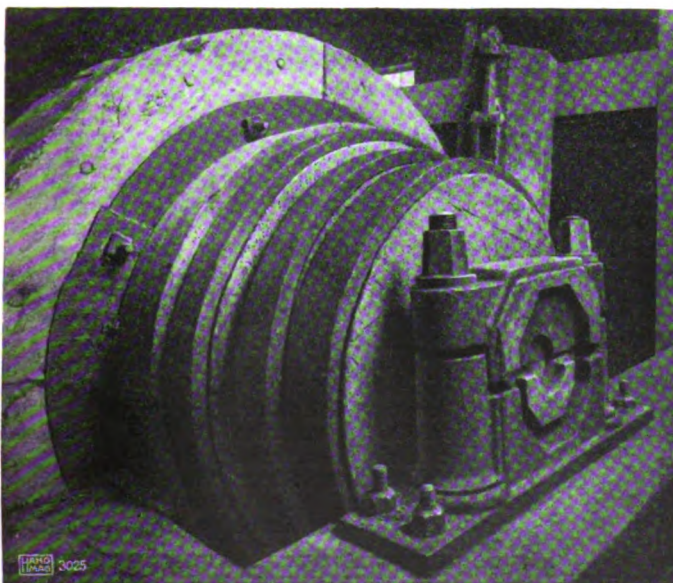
Außenlager einer Wasserradwelle der Wasserkunst in Herrenhausen (Erbaut 1718–1721)
